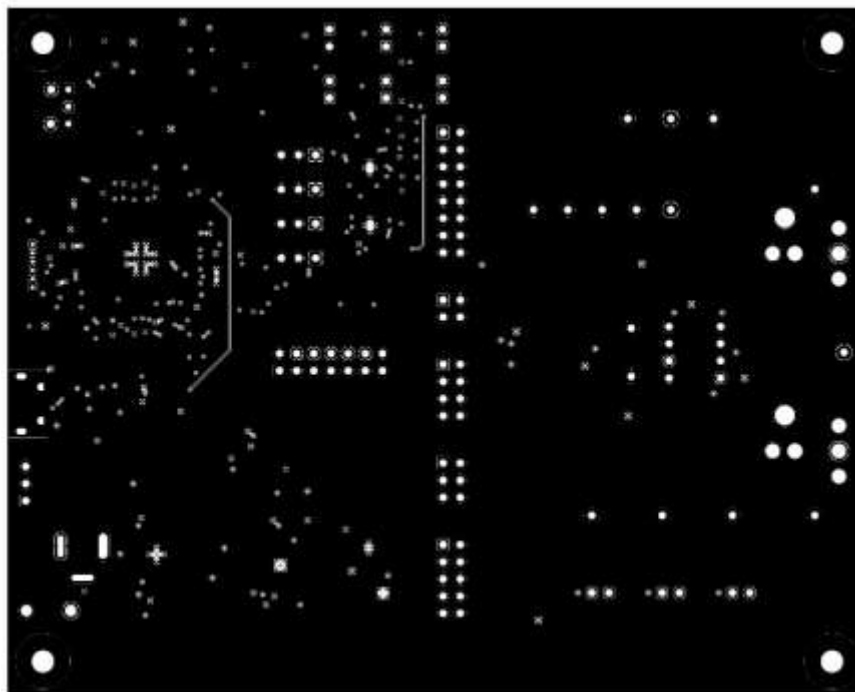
PCM175xEVM PCB の中間層 1 レイアウト (グラウンドプレーン)
